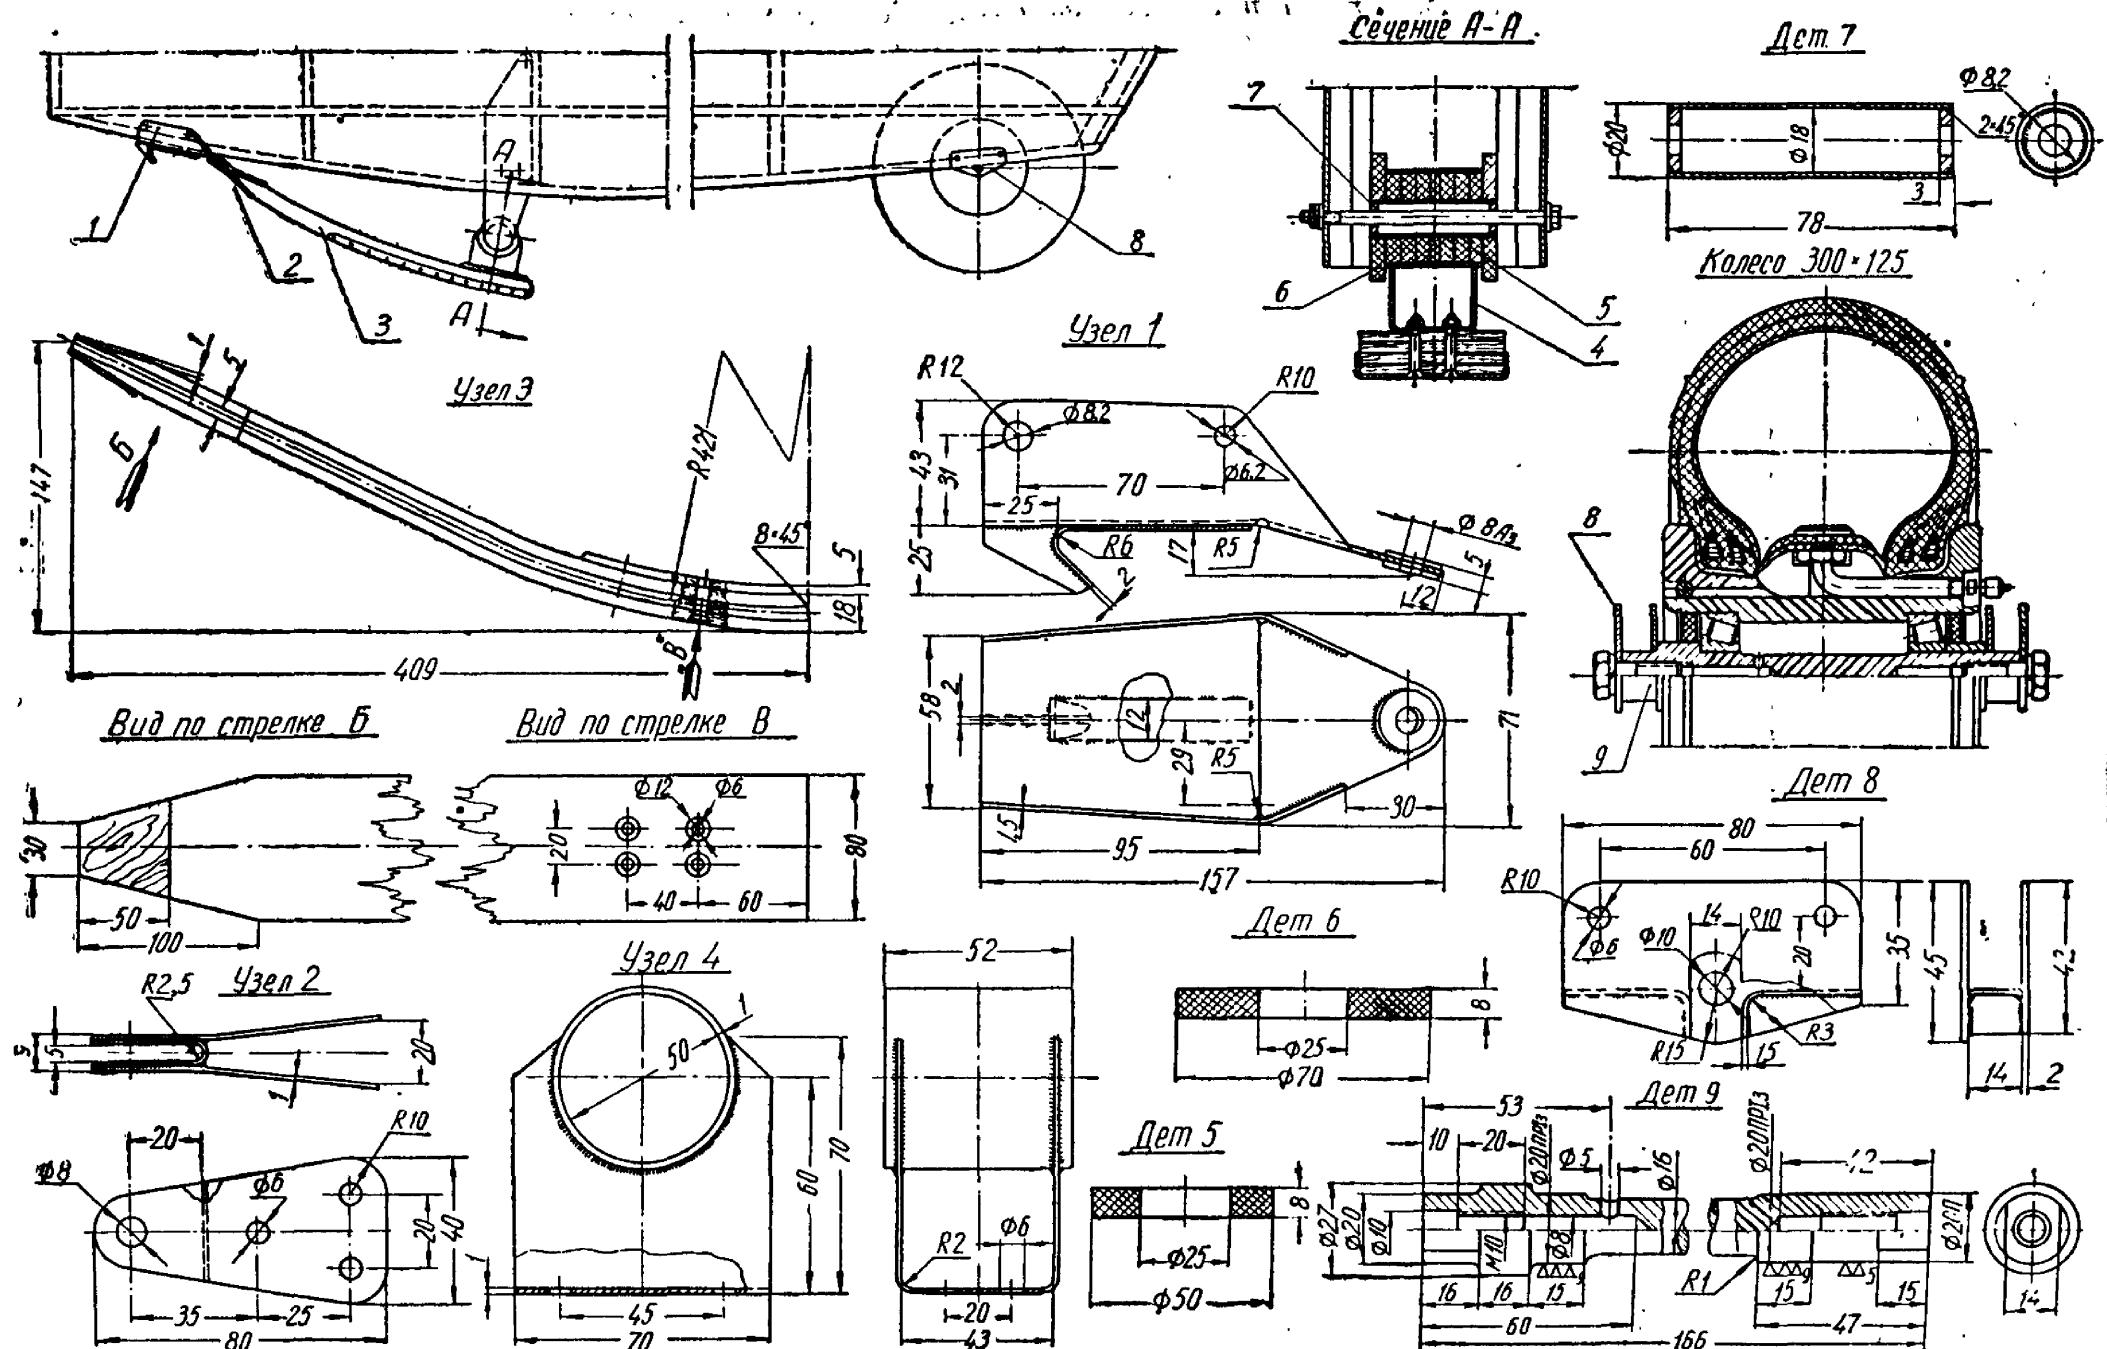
Планер БРО-9. Установка лыжи и колеса
